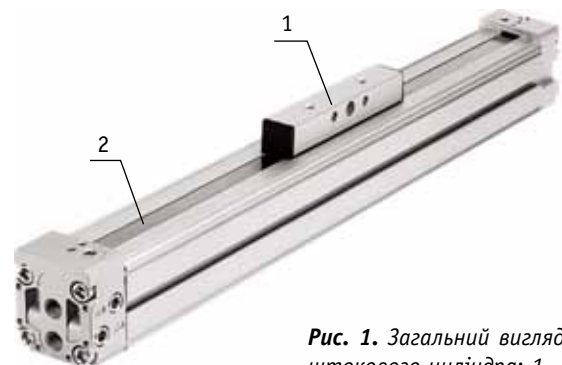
Загальний вигляд безштокового циліндра: 1 — каретка; 2 — корпус
